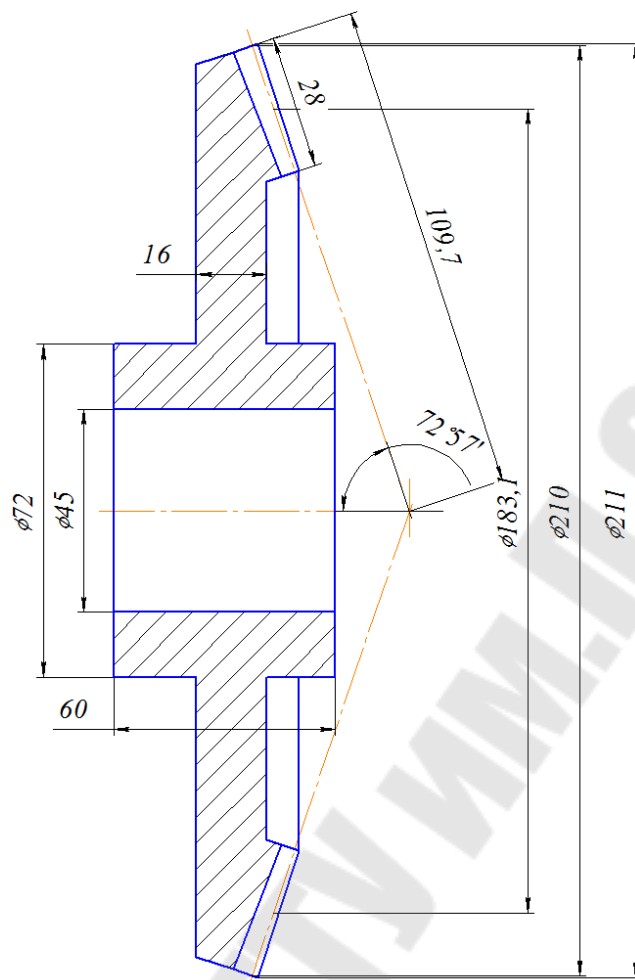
Эскиз зубчатого конического колеса быстроходной ступени редуктора
